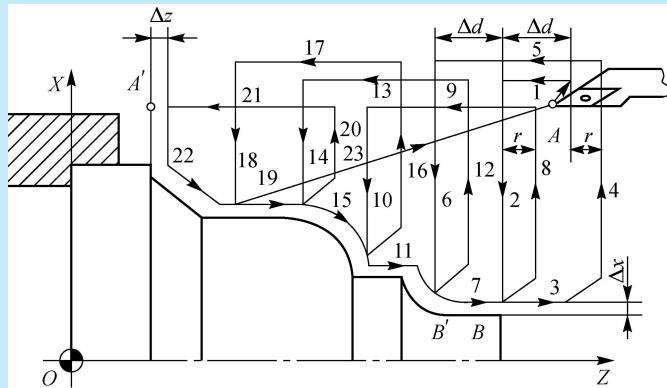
端面粗车复合循环指令 G72 加工轨迹
